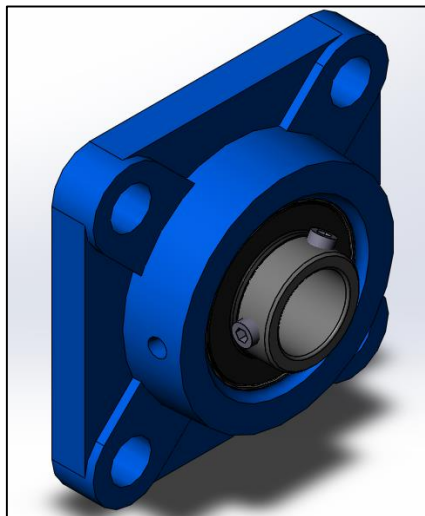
Imagen ilustrativa del soporte axial de rodamiento.
